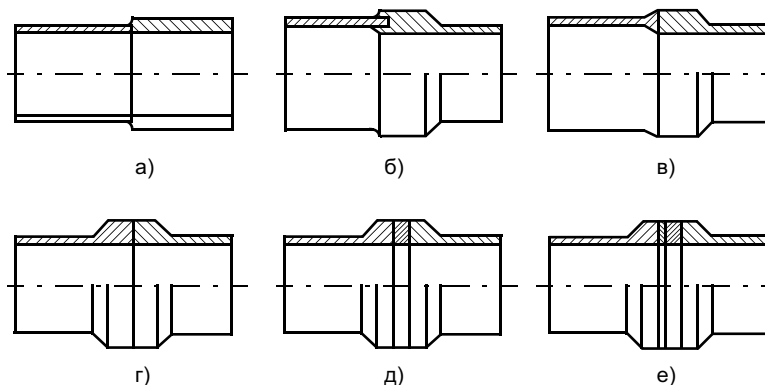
Конструкции стыков сварных соединений трубных переходников
